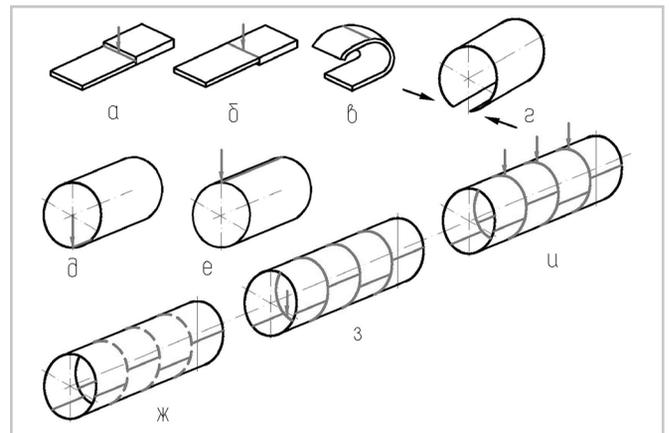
Схема технологического процесса изготовления обечайки из 4-х царг: а – сборка и автоматическая сварка первой стороны развертки царги из 2-х частей; б – автоматическая сварка второй стороны развертки царги; в – вальцовка царги; г – сборка замыкающего стыка царги; д – автоматическая сварка внутреннего шва замыкающего стыка царги; е – автоматическая сварка наружного шва замыкающего стыка царги; ж – сборка обечайки из 4-х царг; з – сварка внутренних кольцевых швов обечайки; и – сварка наружных кольцевых швов обечайки
